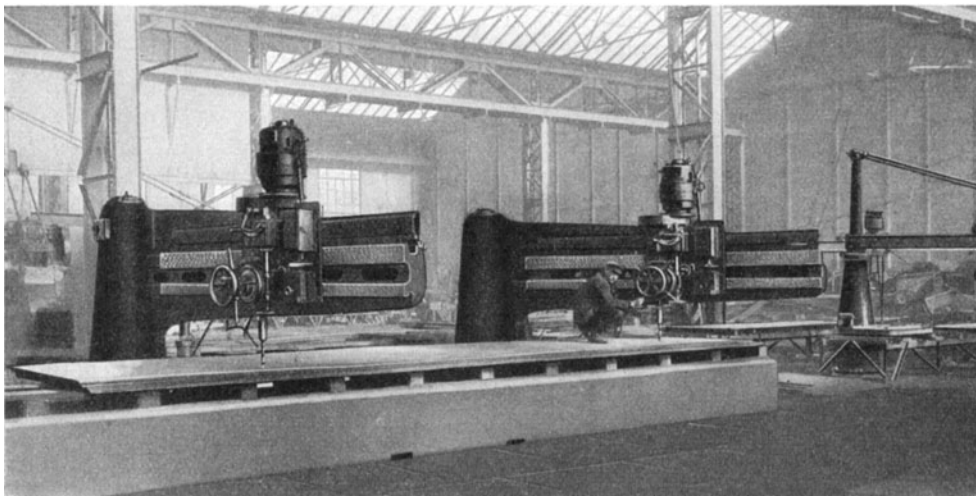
Bohranlage zum Bohren von Blechpaketen.
